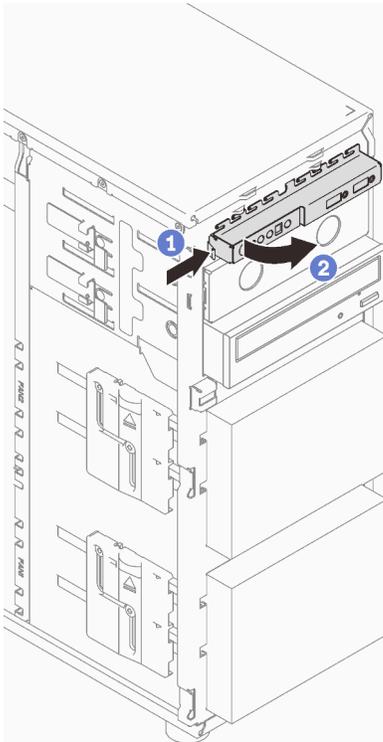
Entfernen der Bedienfeldbaugruppe
